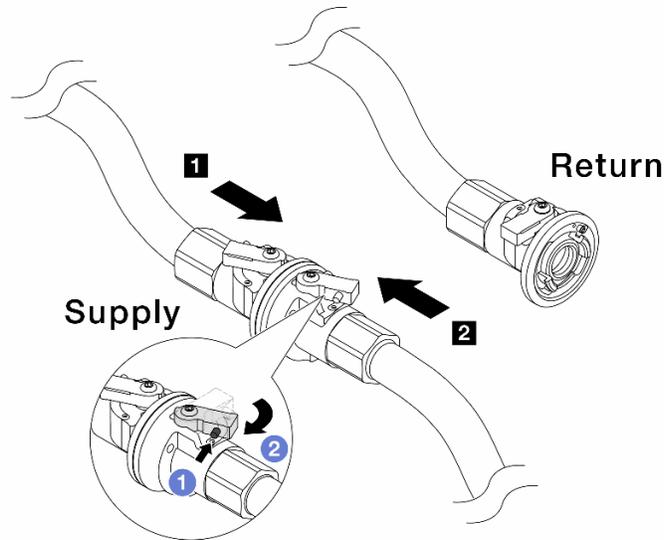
Alimentazione dell'impianto ad alimentazione del collettore
